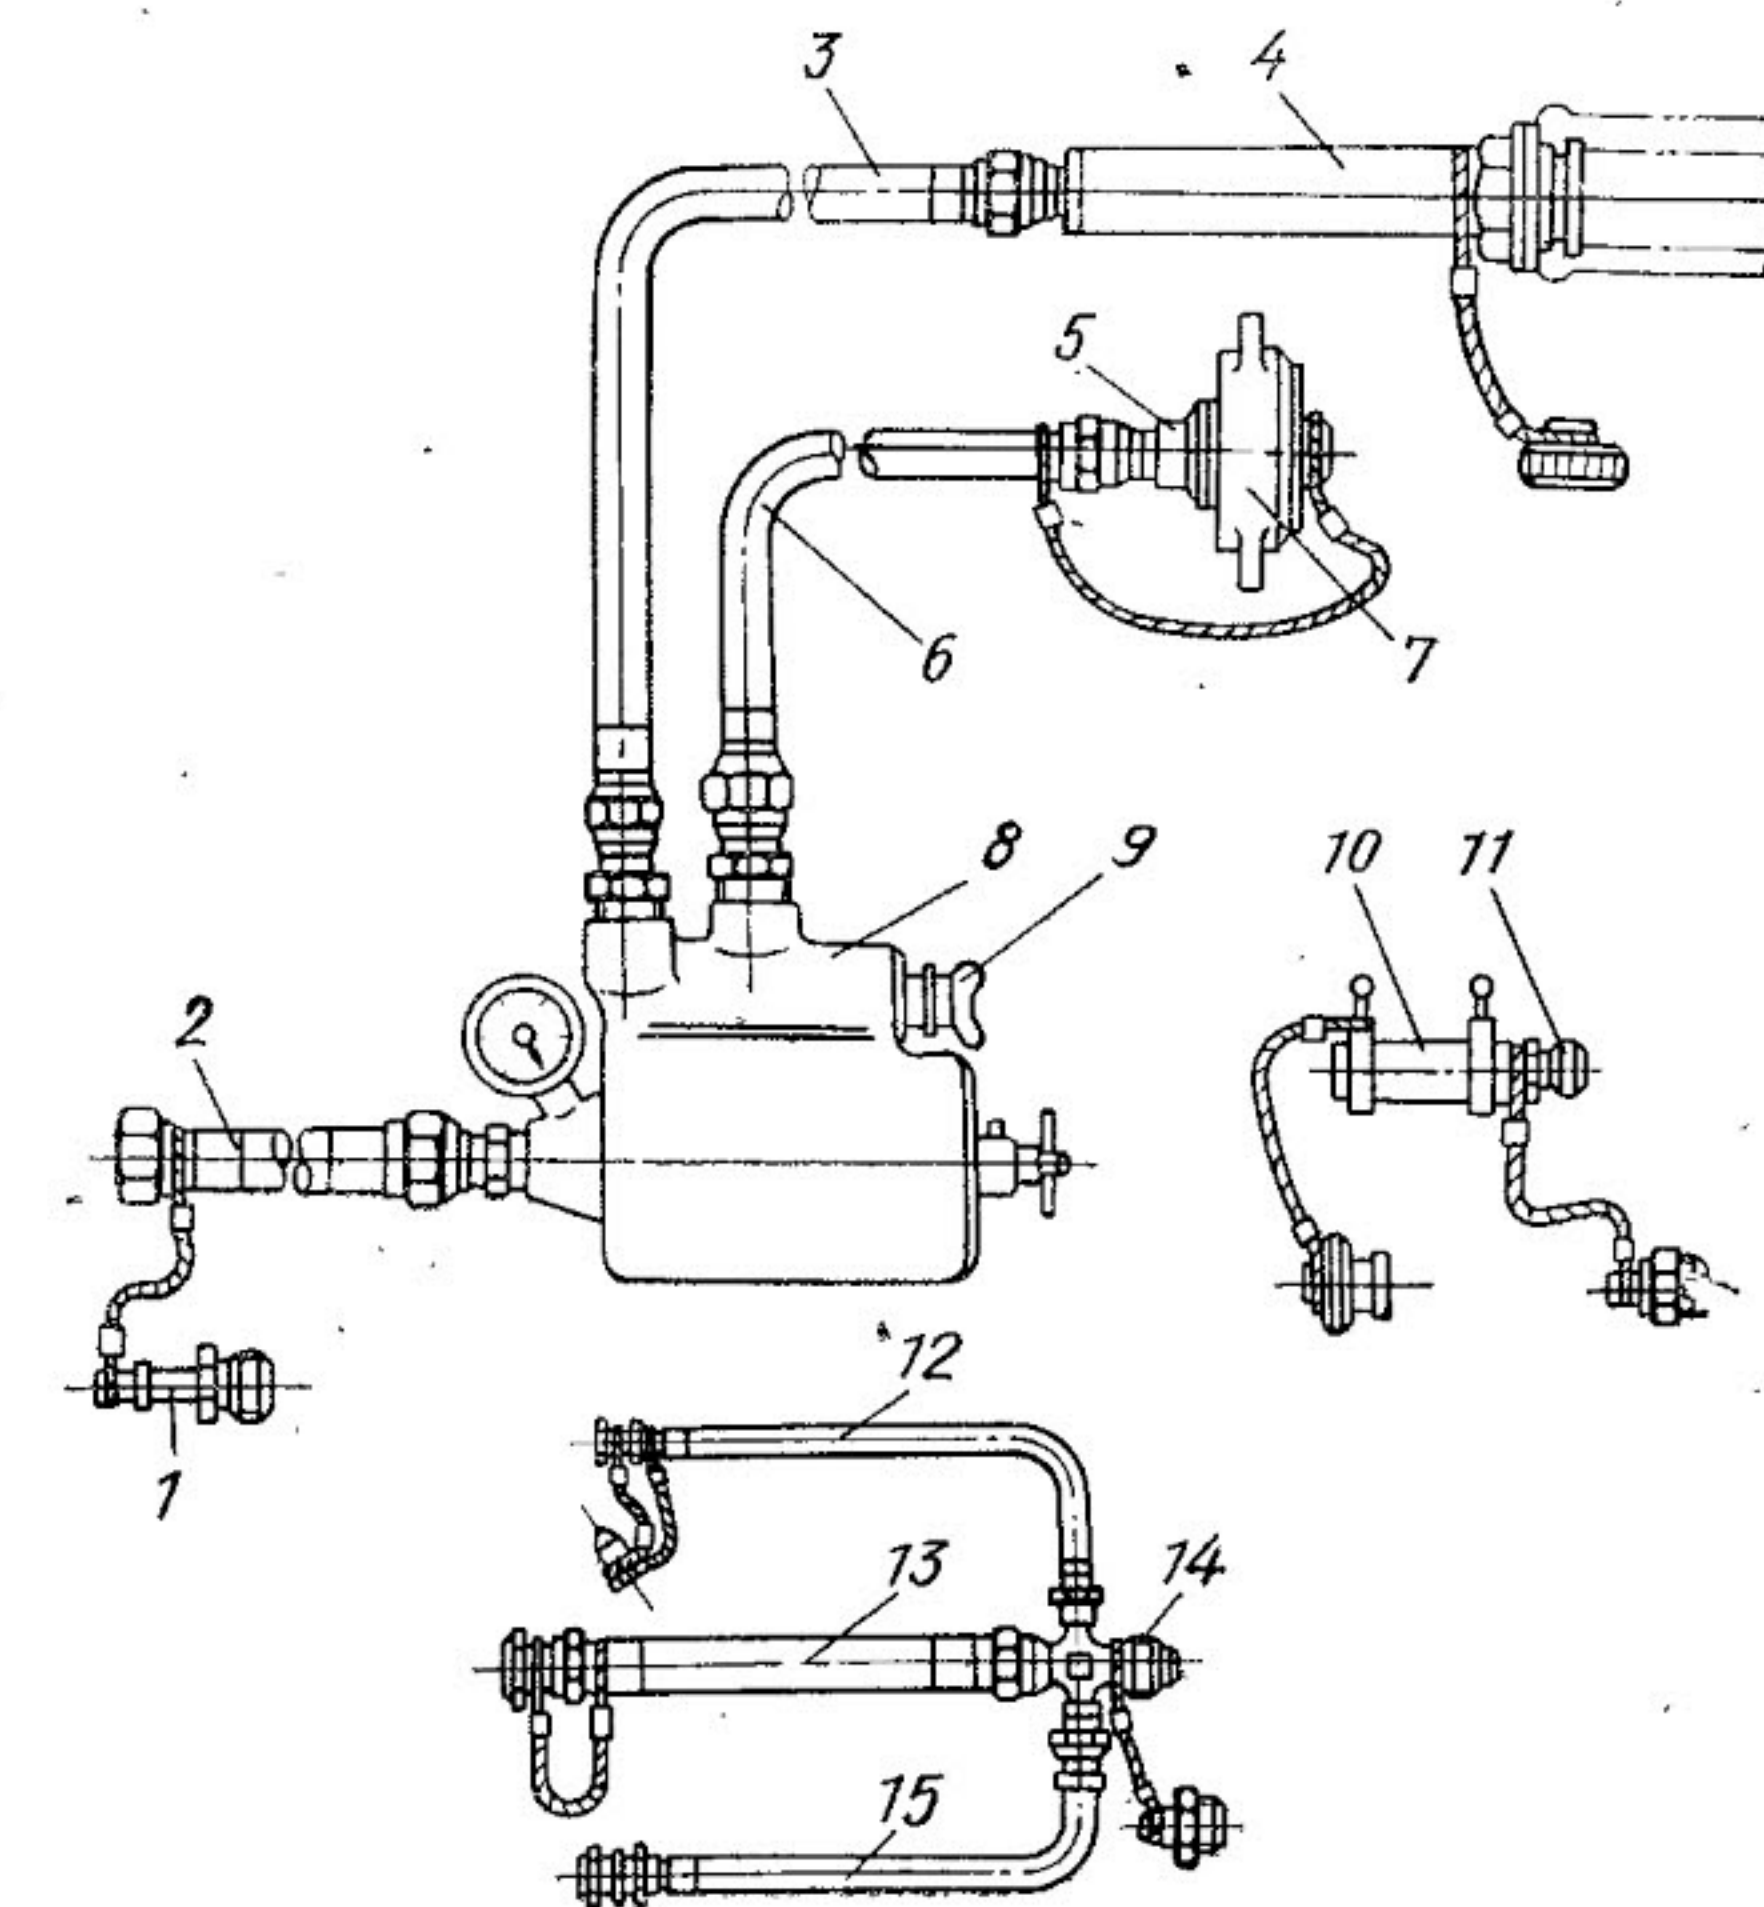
Приспособление для консервации топливной системы двигателя Д-25В, его агрегатов и турбогенератора АИ-8 от МЗ-150:
